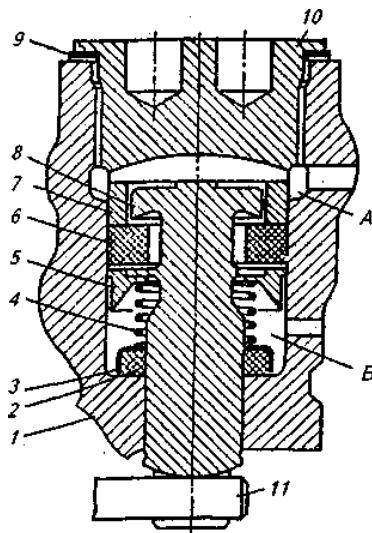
Регулятор давления автомобиля ВАЗ-2121: А, Б- полости регулятора; 1 —корпус; 2—уплотнительное кольцо; 3—обойма; 4— пружина; 5—тарелка; 6 — резиновый уплотнитель; 7-распорная втулка; 8— поршень; 9—прокладка; 10— пробка; 11 — торсион привода регулятора
